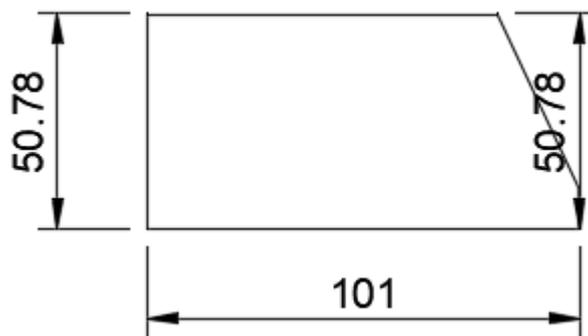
Medidas de la vista lateral, parte superior del diseño en 3D
